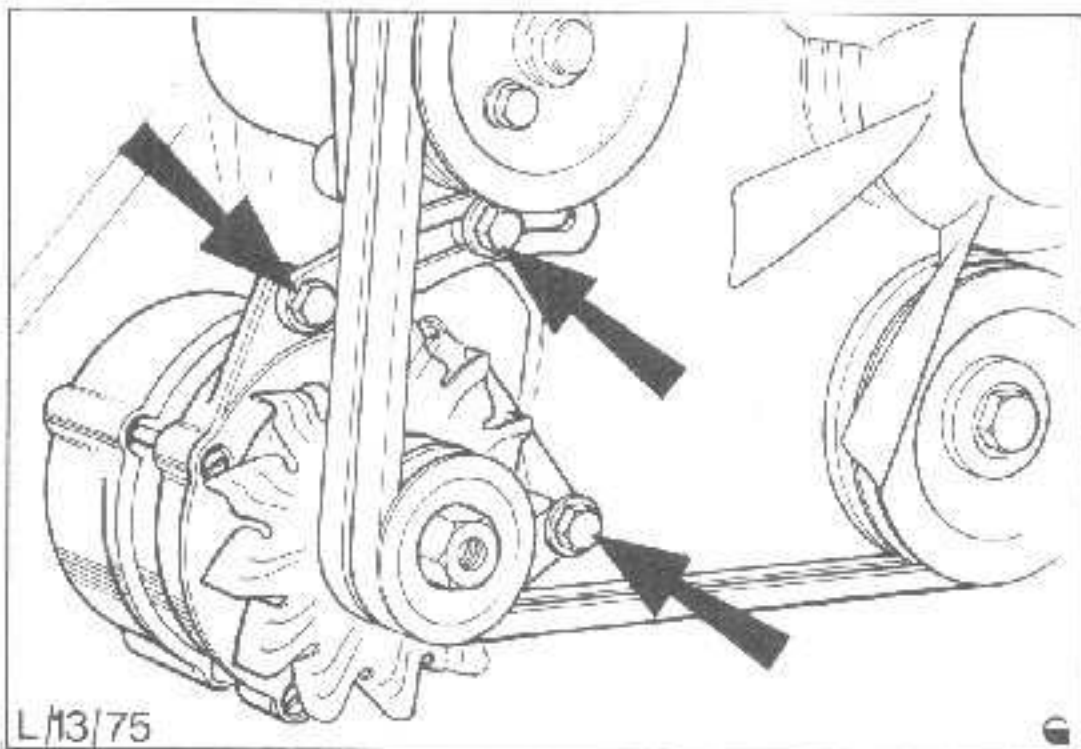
Befestigungsschrauben der Lichtmaschine (OHC-Motor)
